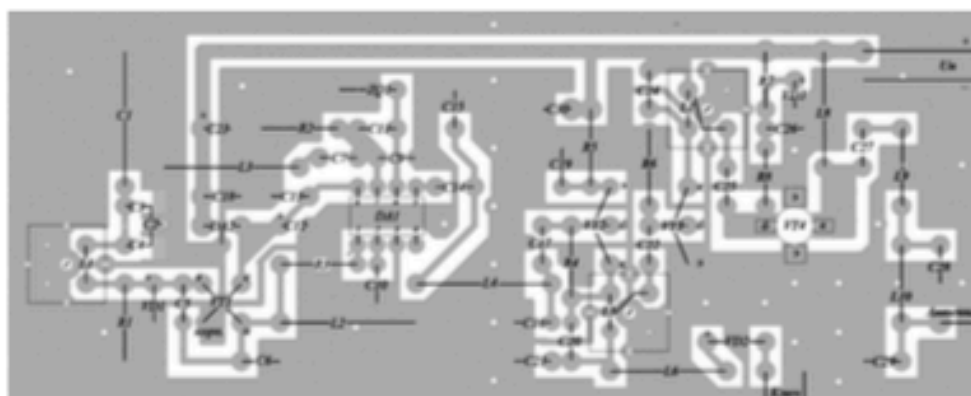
Эскиз монтажной платы передатчика. Вид со стороны расположения деталей
